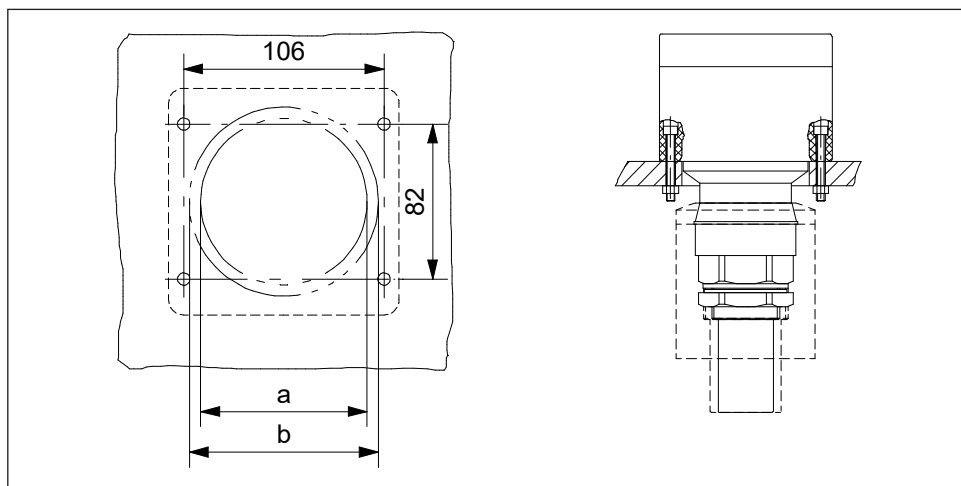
Montage über Befestigung des Elektronikgehäuses
